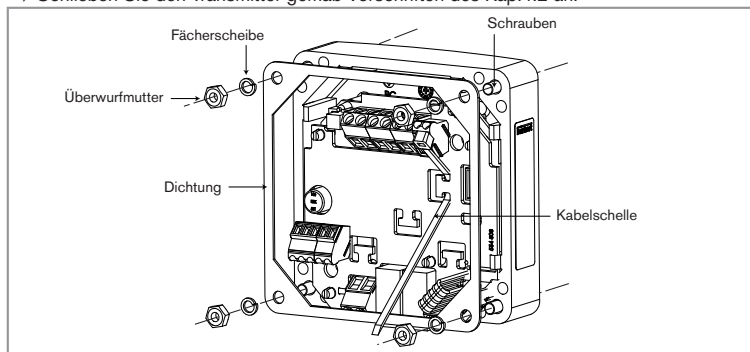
Installation des 8025 Schaltschrank-Ausführung
